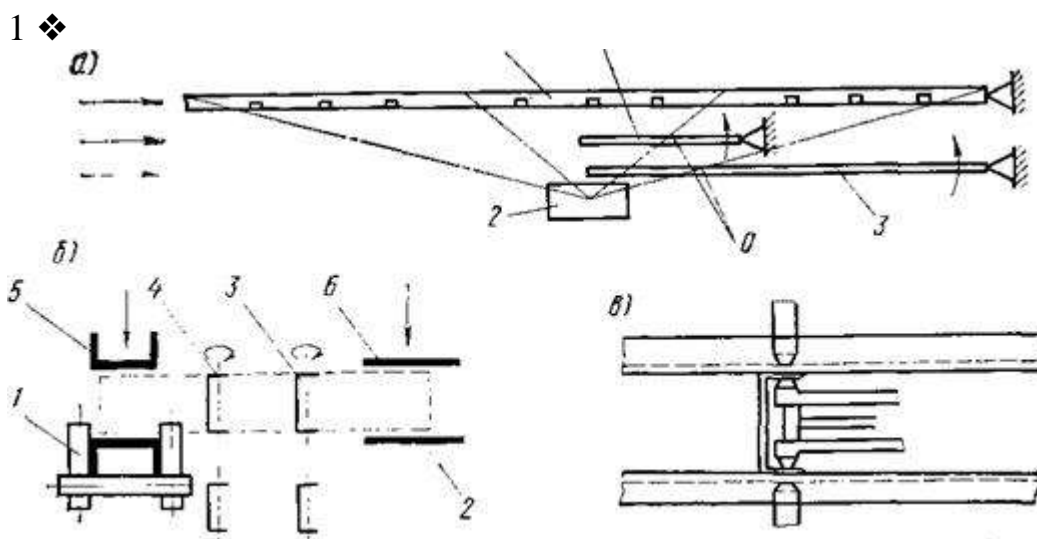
Схема изготовления типовых стропильных ферм вставляемых между стенками верхнего пояса. По окончании сварки специальными выталкивателями, ферма извлекается из кондуктора, приемные секции кондуктора возвращаются в исходное положение.
